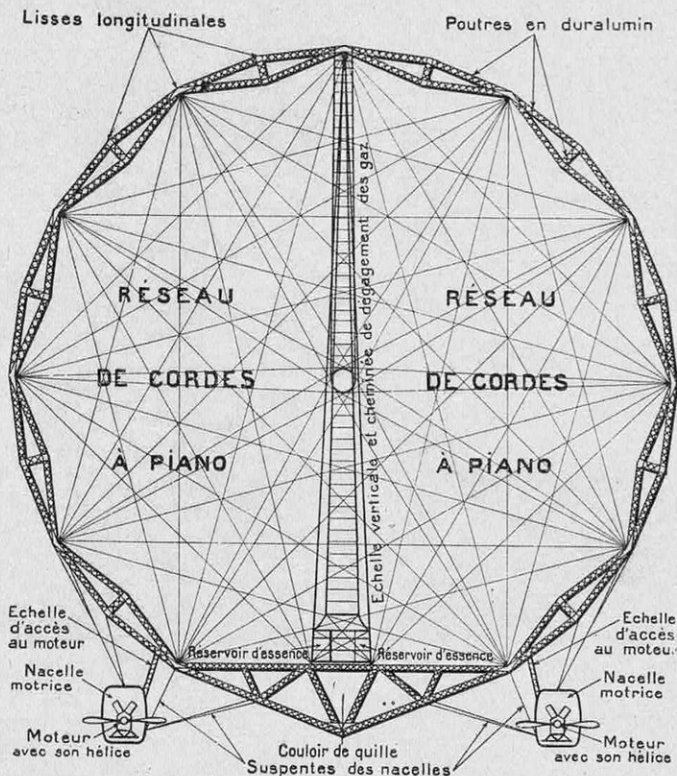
COUPE TRANSVERSALE VERTICALE DU « LOS-ANGELES » SUIVANT UN ANNEAU PRINCIPAL
